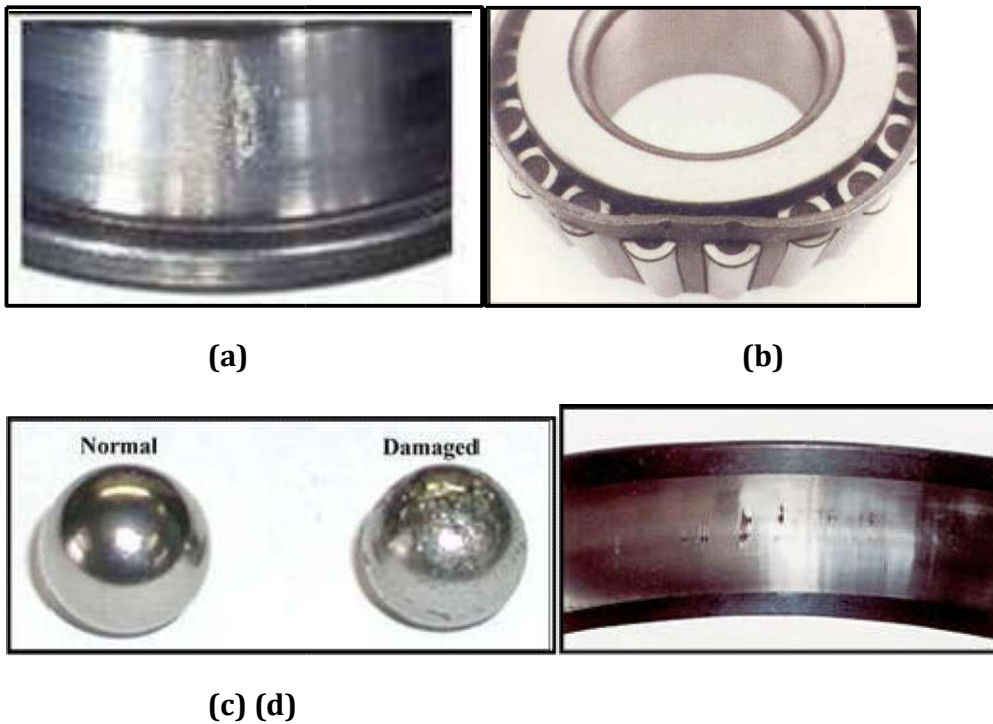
Défauts des roulements à billes. (a) sur la bague interne; (b) sur la cage; (c) sur une bille et (d) sur la bague externe [28].
